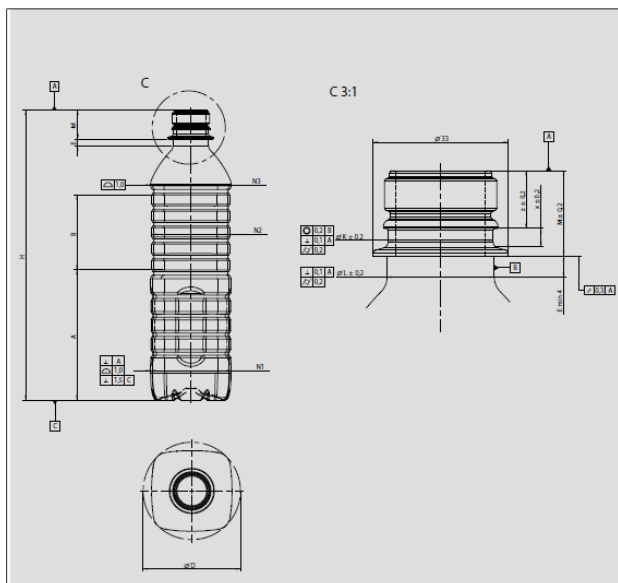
РЕТ-сосуд с габаритными размерами (форматный сосуд)
